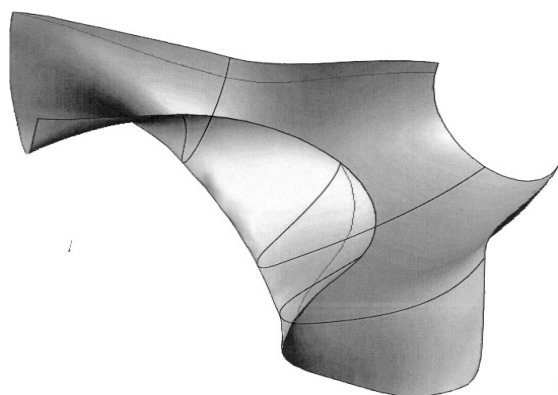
Типовой фрагмент вакуумной камеры «Стеллоратора», заготовка для которого состоит из 4-х элементар-
